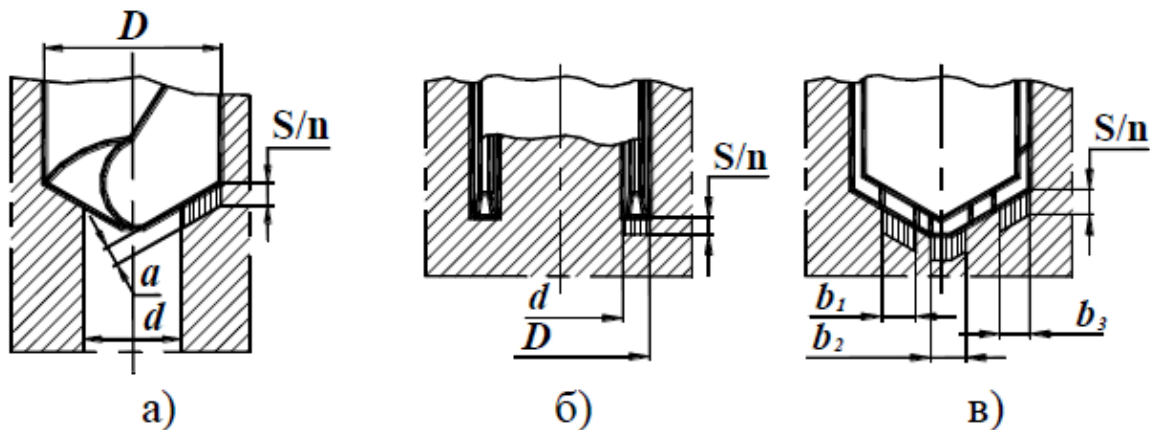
Схема зрізуваного шару при: (а) розсвердленні, (б) кільцевому свердлінні та (в) багатокромковому свердлінні
